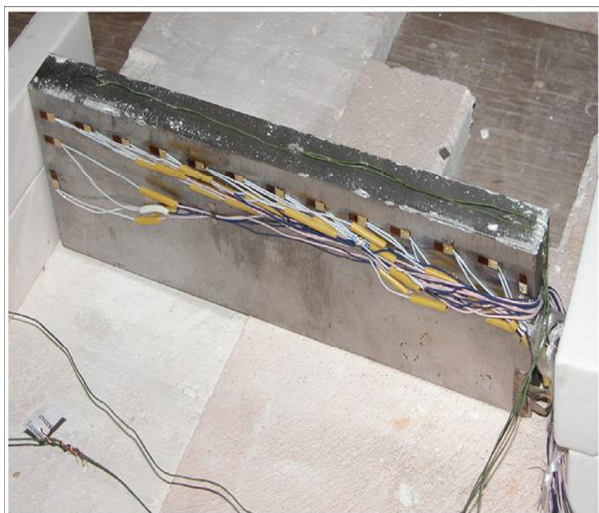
Заготовка с термометрами, используемая для калибровки и первоначального эксперимента
